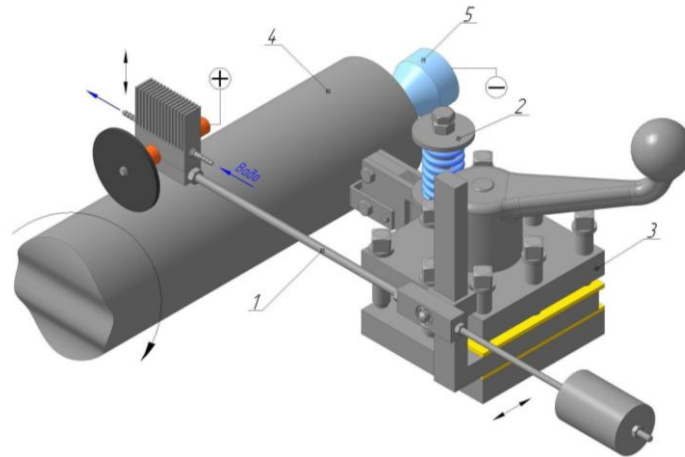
Тривимірна модель-схема установки для формування комбінованого зносостійкого покриття на деталях типу вал: 1 – пристрій для ЕІЛ; 2 – пристрій для обкочування; 3 – супорт токарно-гвинторізного верстату; 4 – оброблювана деталь; 5 – центр з електричним контактом
